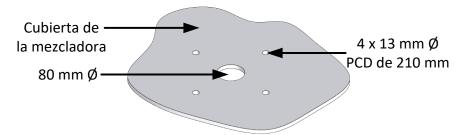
Cubierta de la mezcladora preparada para el conector giratorio
